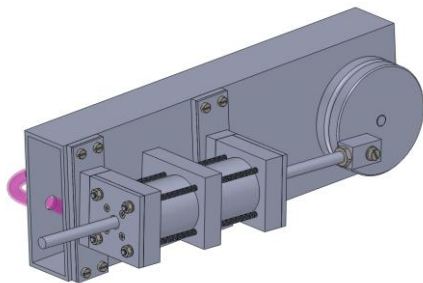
Prototyp membránové elektrocentrály bez řemenice a alternátoru
